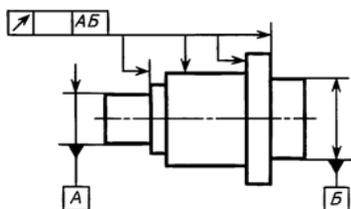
Обозначение повторяющихся допусков
